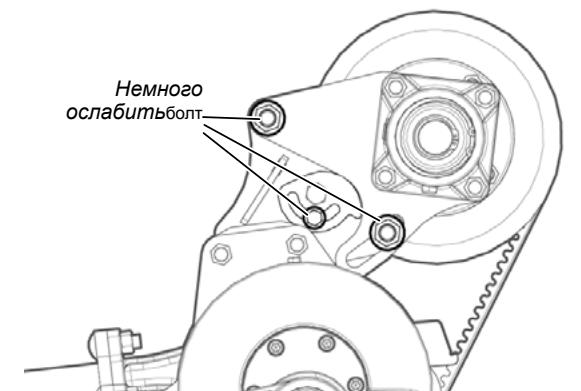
Натяжение ремня ножей: ослабление стопорной гайки и болта.
